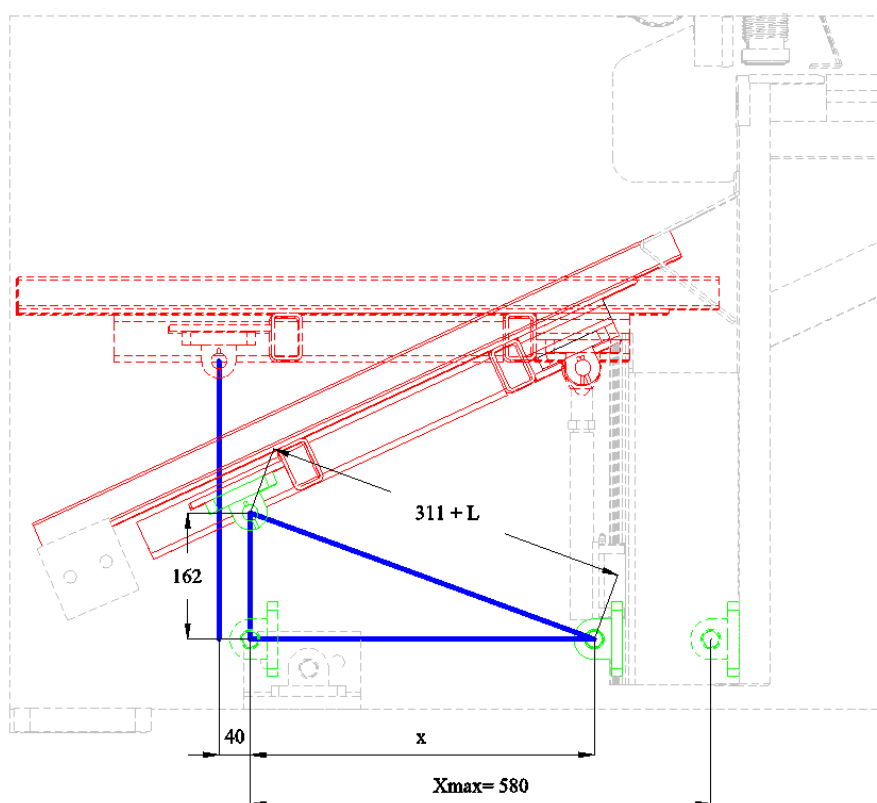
Cilindros servo pneumático - Posição B – “Descarga” (dimensões em mm)
